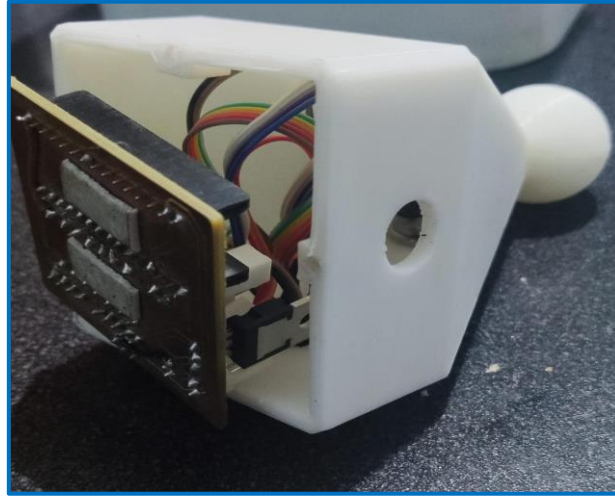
Soldadura del nodo Transmisor
